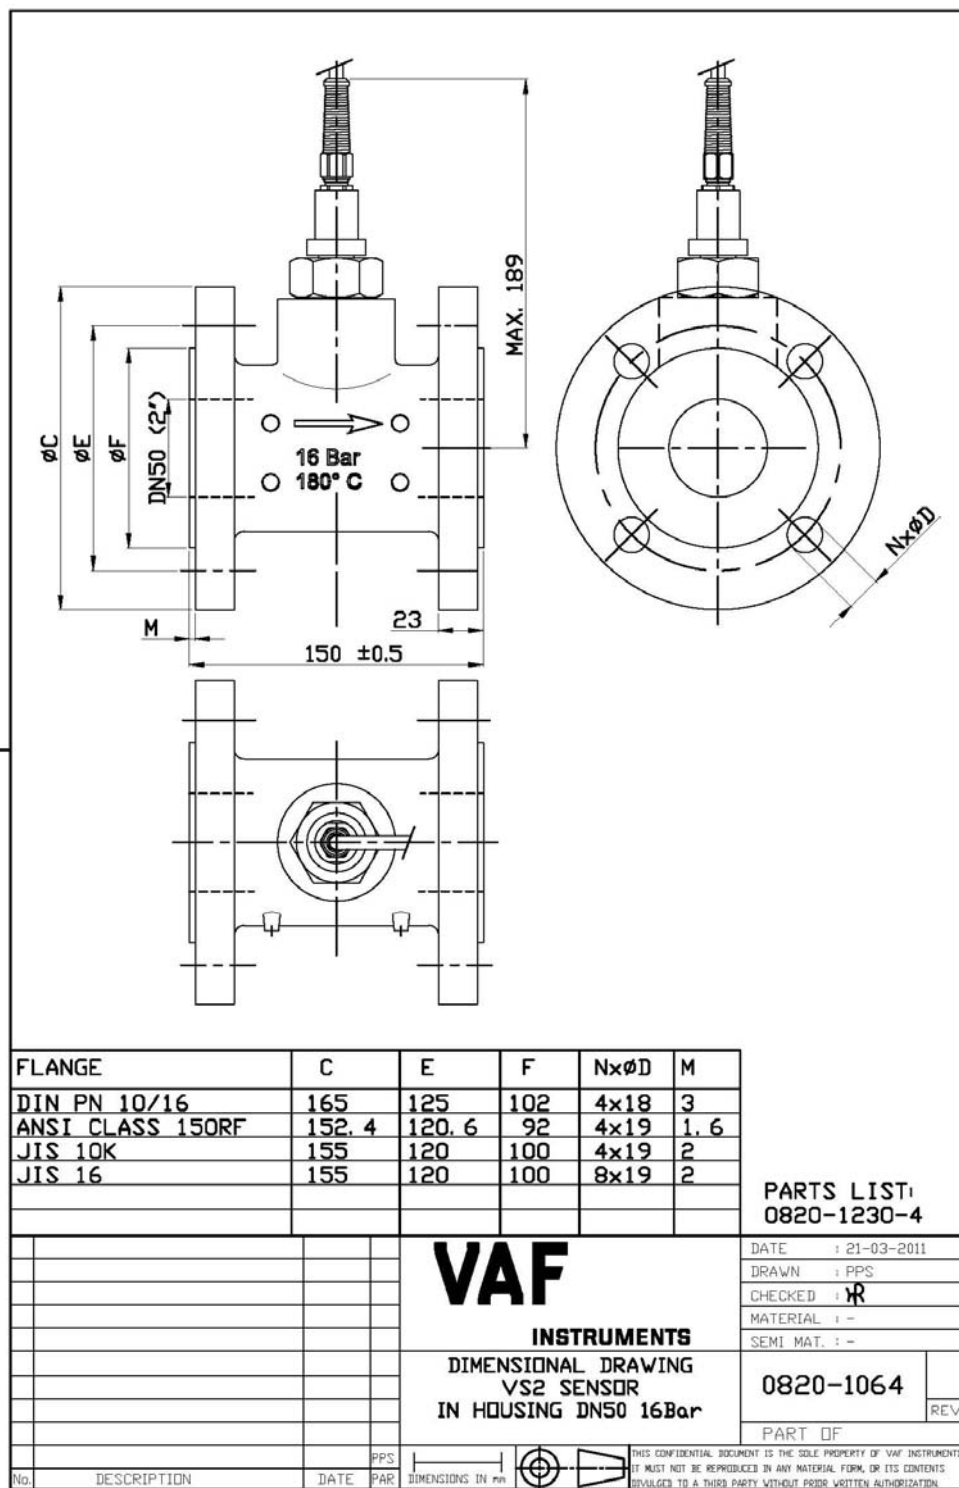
Dimensioni del sensore ViscoSense®2 (Tutte le dimensioni sono in millimetri).
